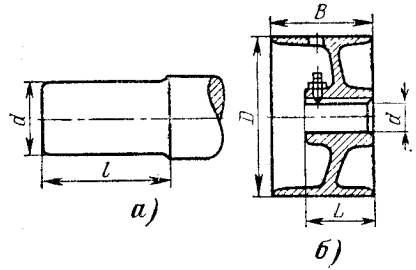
Цилиндрический конец вала двигателя (а) и ременный шкив (б).
